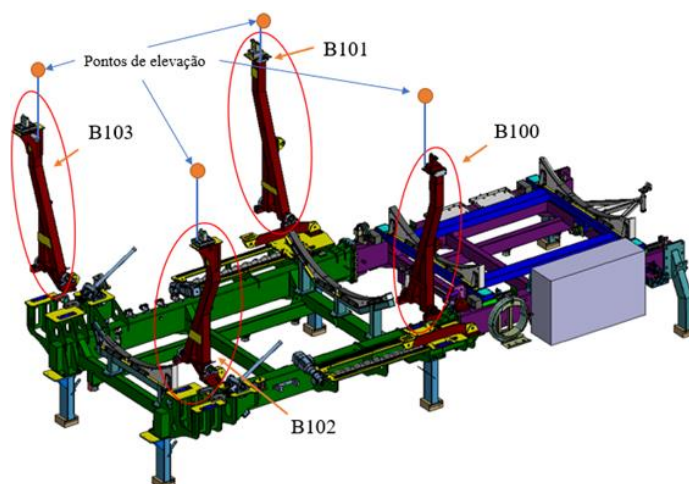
Pontos de elevação dos braços da PALLETE 13-14.
